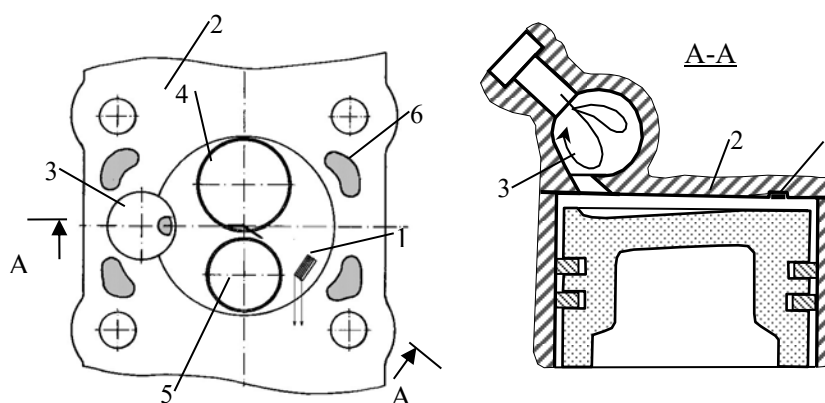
Место установки ГДТП на поверхности крышки блока цилиндров:
